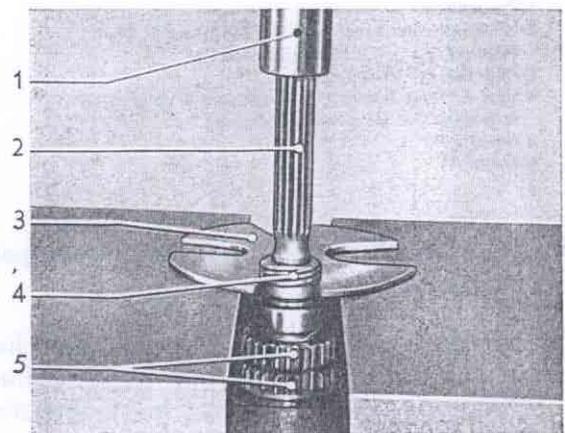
Tachometerschraubenrad von Hauptwelle abdrücken
